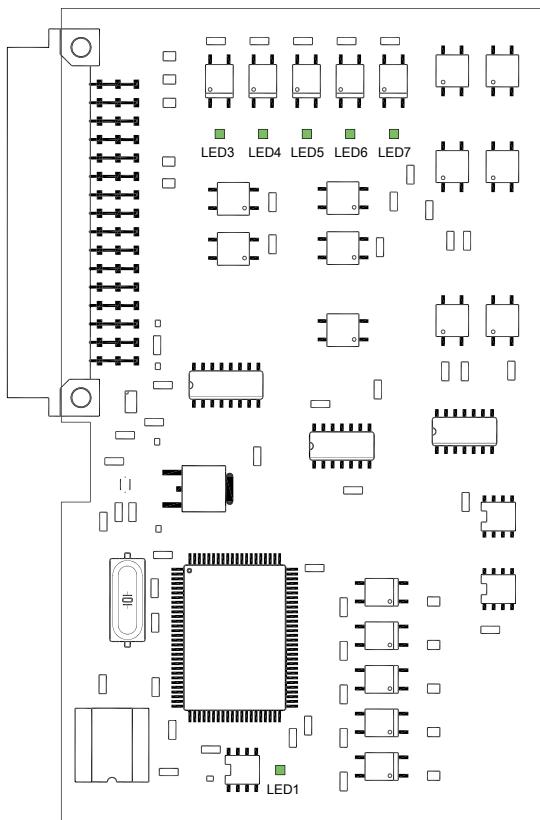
ไฟ LED ในการควบคุม applicator PCB
